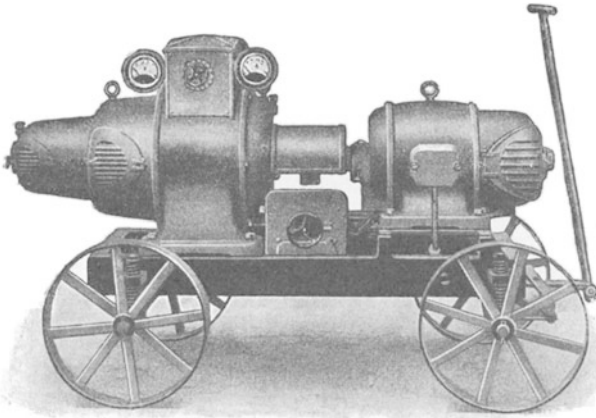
Fahrbarer Schweißumformer mit Erregermaschine (links).
